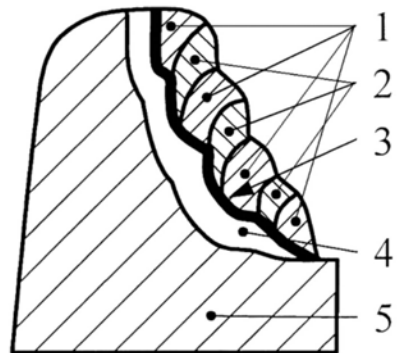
Переріз гребеня вагонного колеса після наплавлення. 1 – наплавлений шар, 2 – зона сплавлення двох шарів, 3 – зона сплавлення основного та наплавленого металу, 4 – зона термічного впливу, 5 – основний метал.
